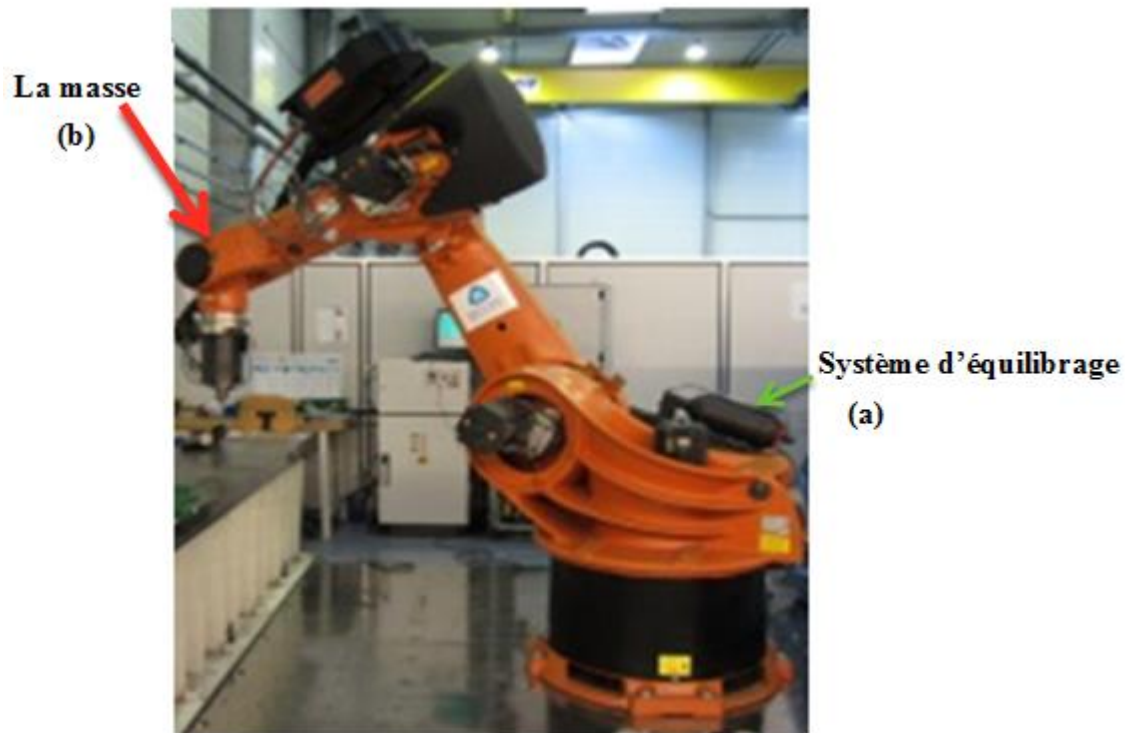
Robot Kuka KR500-2MT de l'Institut de Soudure de Goin
